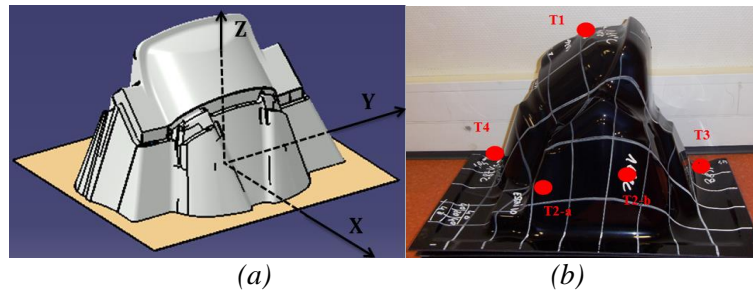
a) Vue 3D du moule carter et b) pièce thermoformée avec positions des thermocouples
